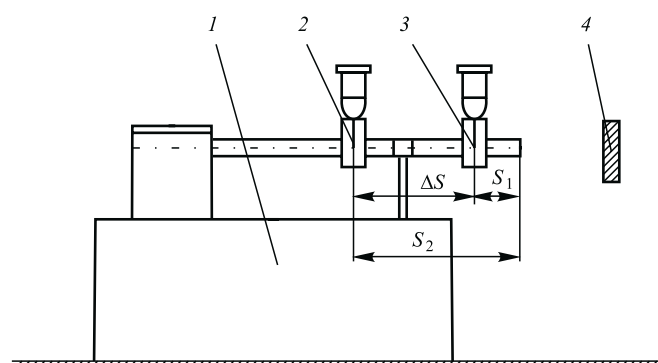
Схема расположения порошковых дозаторов при напылении с синхронной абразивной подготовкой подложки:
